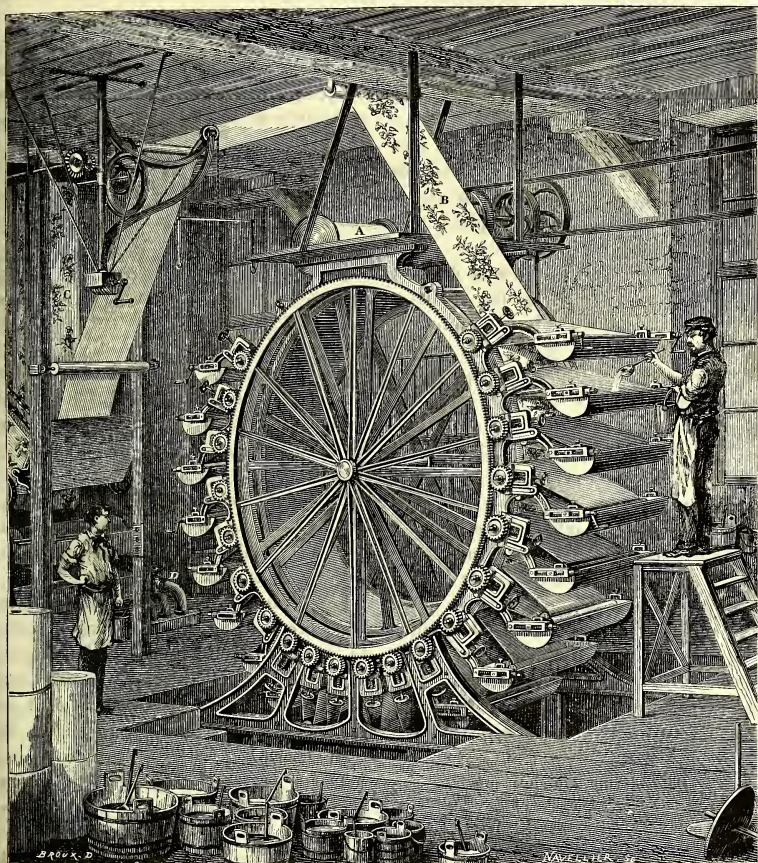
Machine à imprimer les papiers peints en 20 couleurs.
